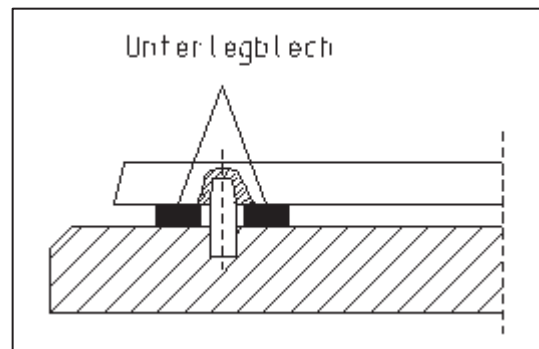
Befestigungsmaterial für Pumpe mit freiem Wellenende
